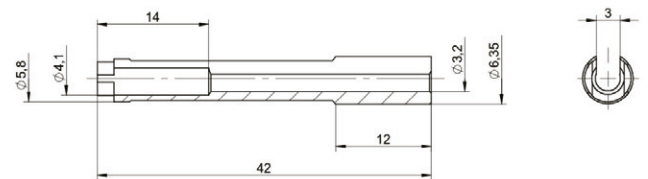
Demontagewerkzeug für Kabel Typ 1300A49
